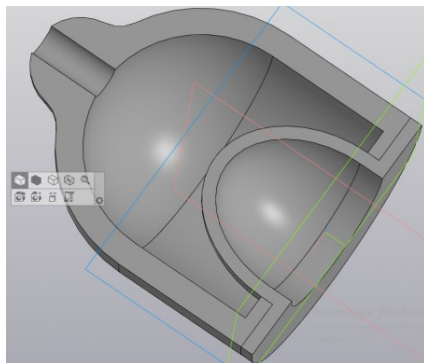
Разрез сборки корпуса кумулятивного заряда
